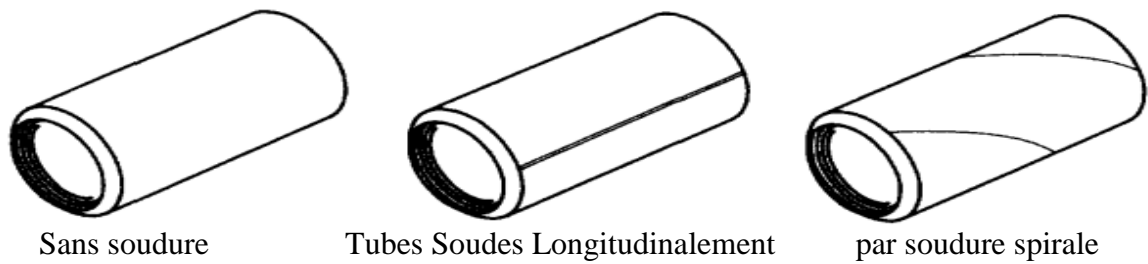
les trois modes de fabrication des tubes soudés [1]
